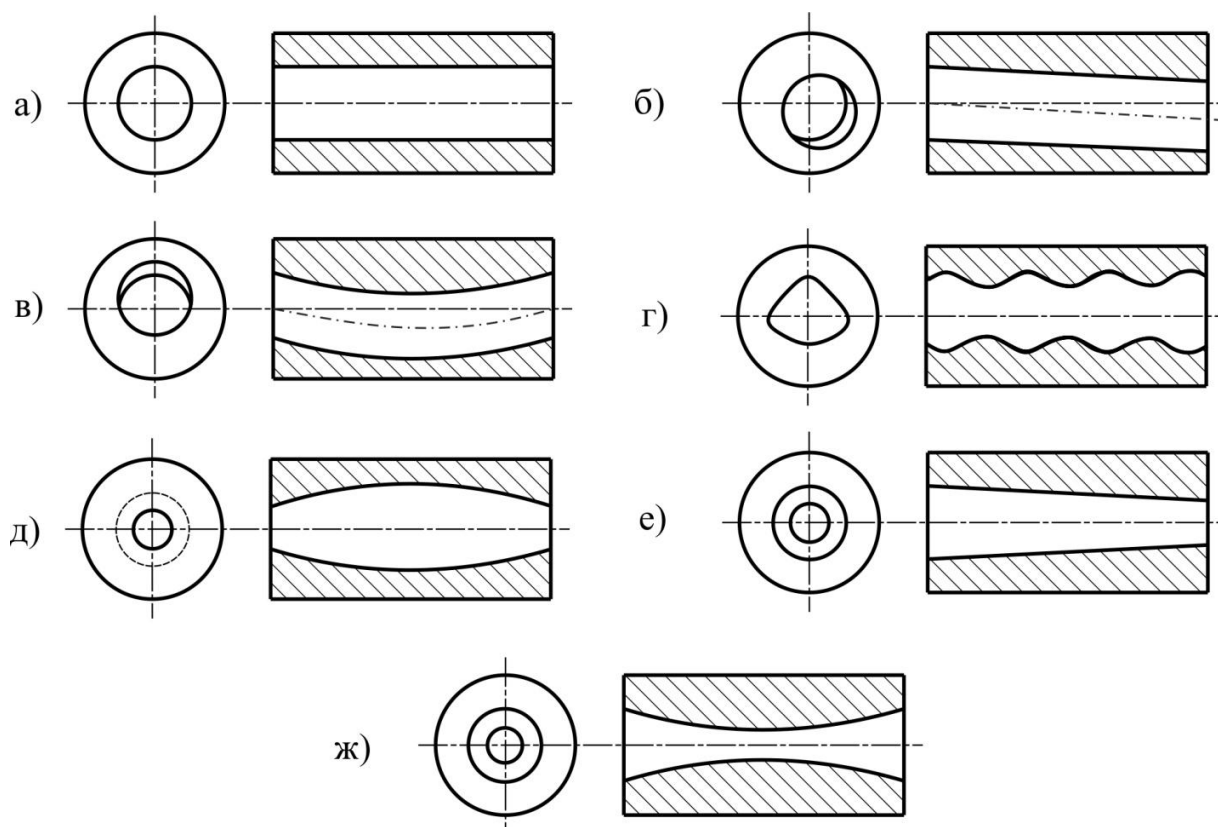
Возможные профили главных отверстий в корпусных деталях:
